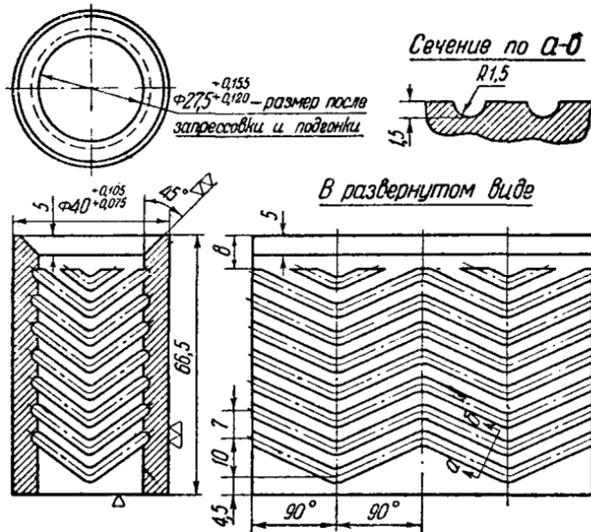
Дет. № 084. Втулка крышки и корпуса водяного насоса
